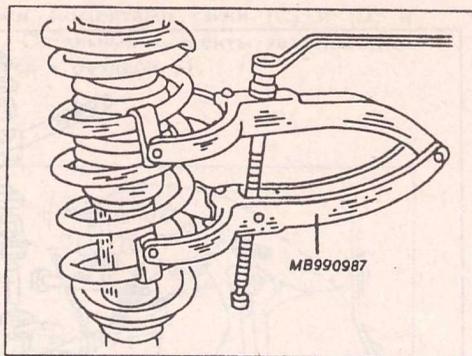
Устройство для сжатия винтовой пружины для разборки амортизационной стойки. На рис. 219 показана маркировка пружин.
